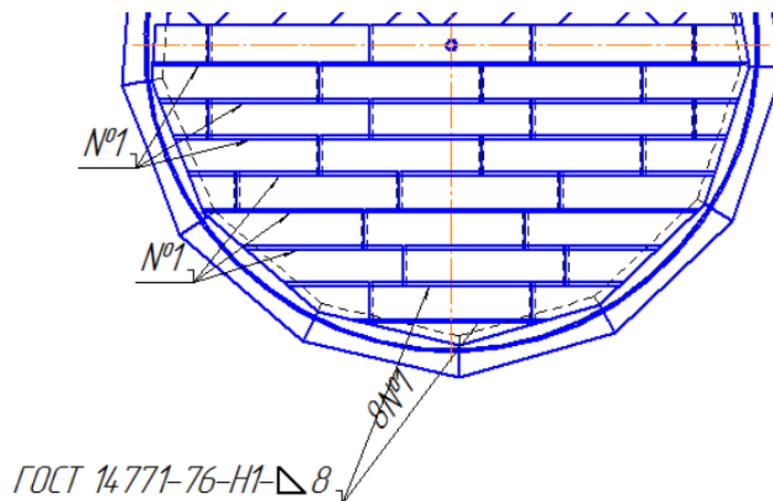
Сварка нахлесточных швов
